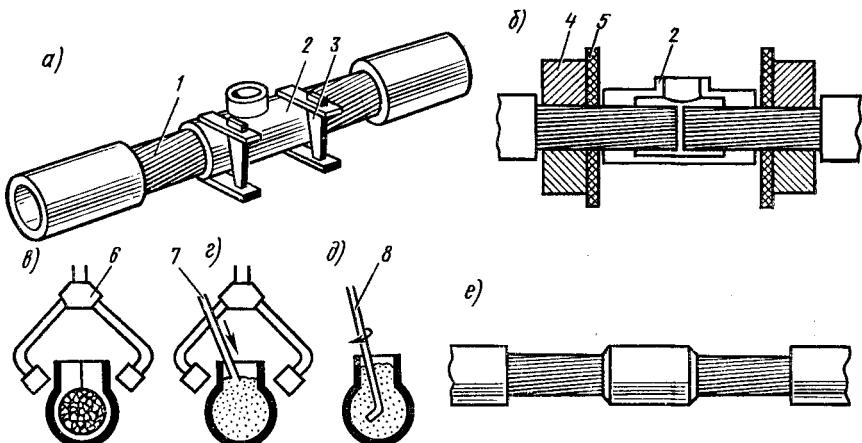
Последовательность операций при пропано-кислородной сварке стыковых соединений жил:
